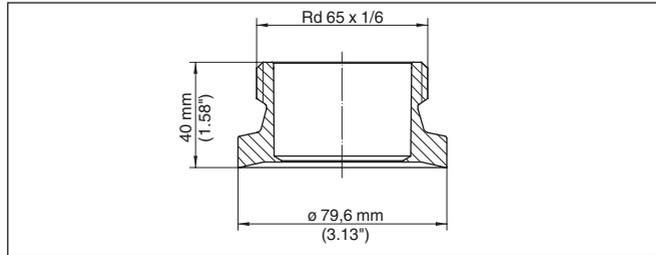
Dimensiones racor para soldar conexión aséptica F40 con tuerca de unión ranurada
